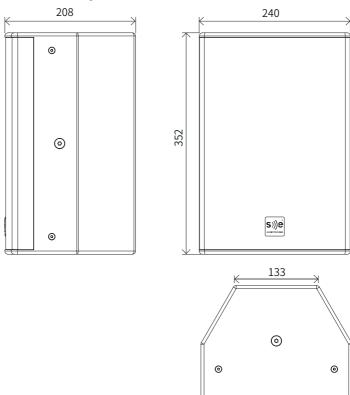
COX 8 MKII Ansichten und Abmessungen. Angaben in Millimetern.
